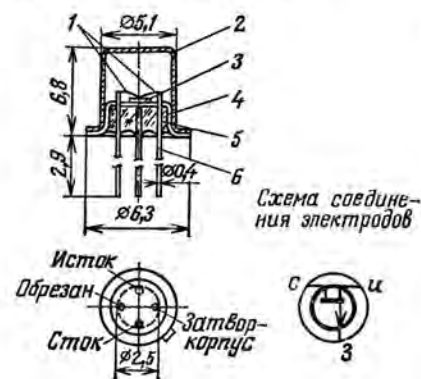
Полевой транзистор КП103 в металлостеклянном корпусе: 1 — золотые проволоки; 2 — корпус; 3 — кристалл; 4 — ножка; 5 — изолятор (стекло) 6 — вывод.
